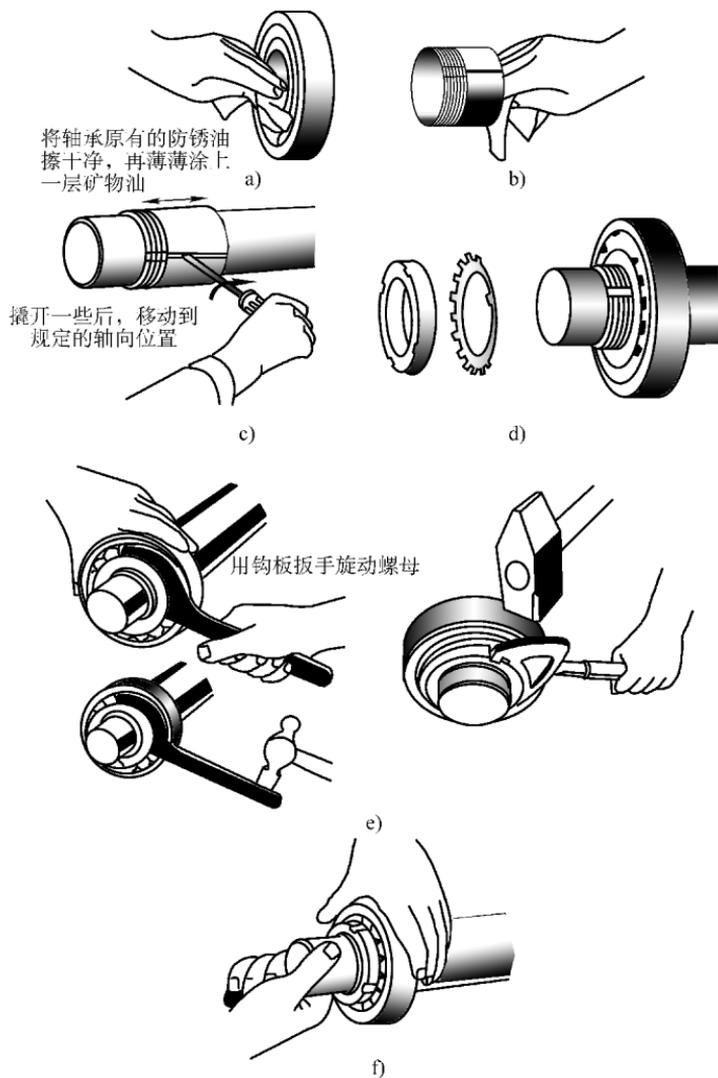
将圆锥内孔轴承安装于圆柱轴上的步骤
